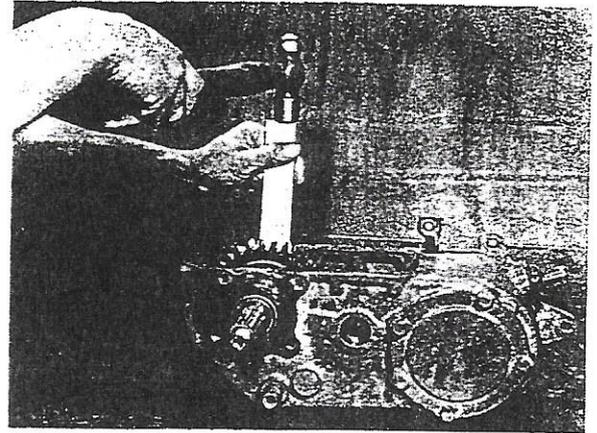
Cunha para desmontagem da pista do rolamento.
